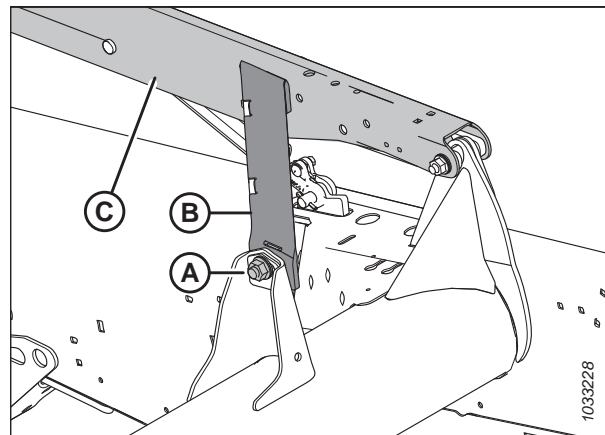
Опорный рычаг мотовила — жатки для неевропейских стран
